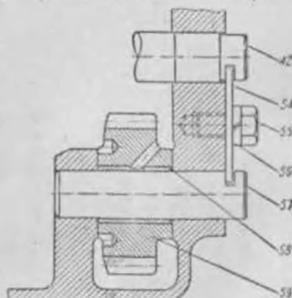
Шестерня заднего хода: 42 — ось промежуточного вала; 44 — стопорная пластина; 45 — блок стопорной пластины; 46 — шайба; 47 — ось шестерни заднего хода; 48 — втулка шестерни заднего хода; 49 — втулка шестерни заднего хода
